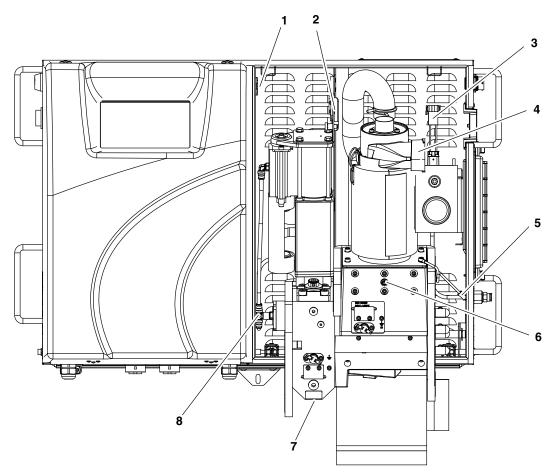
Vorbereitungen zum Entfernen der Hydraulikbaugruppe
